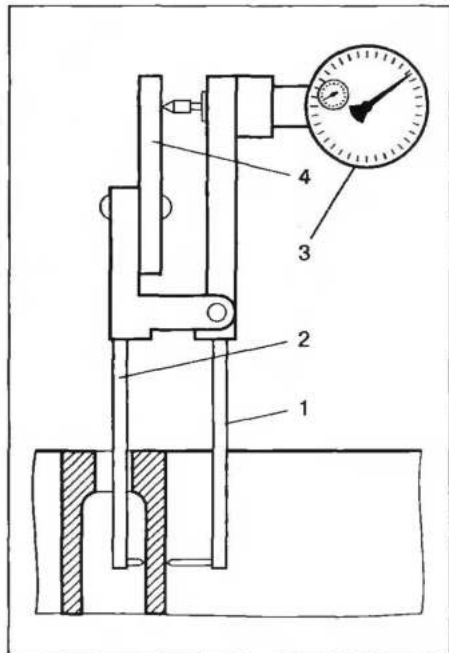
Схема измерения толщины стенки цилиндра блока стенкомером: 1, 2 — ножка приспособления; 3 — индикатор часового типа; 4 — поворотный упор
